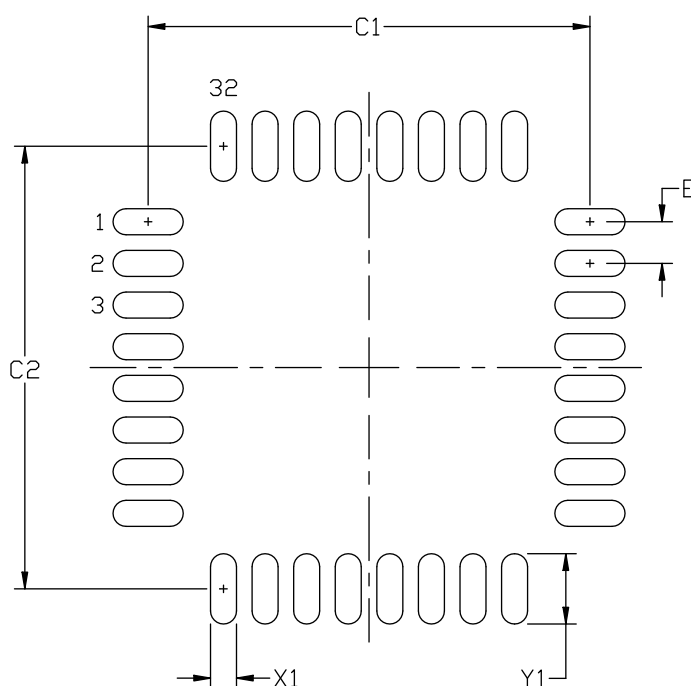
QFP32 PCB 焊盘布局图
